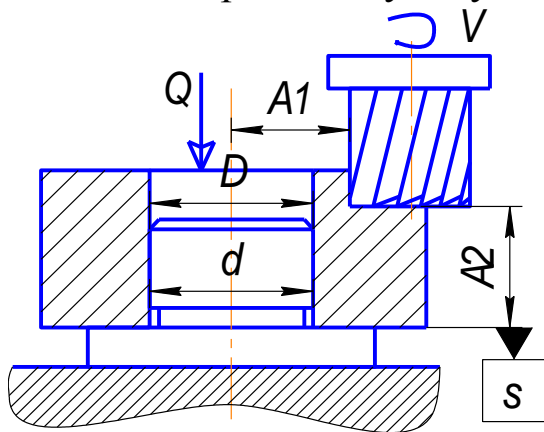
Схема фрезерования втулки (к задаче 1)
